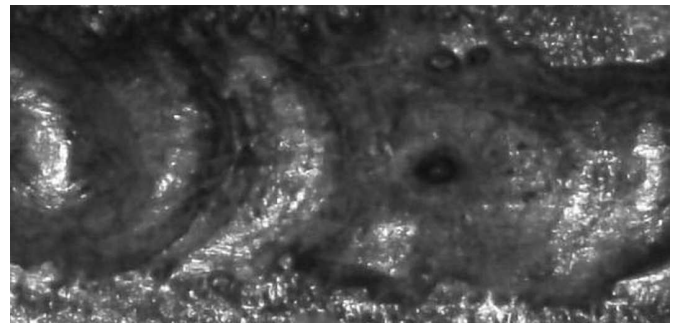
Крупные поверхностные поры в сварном шве
